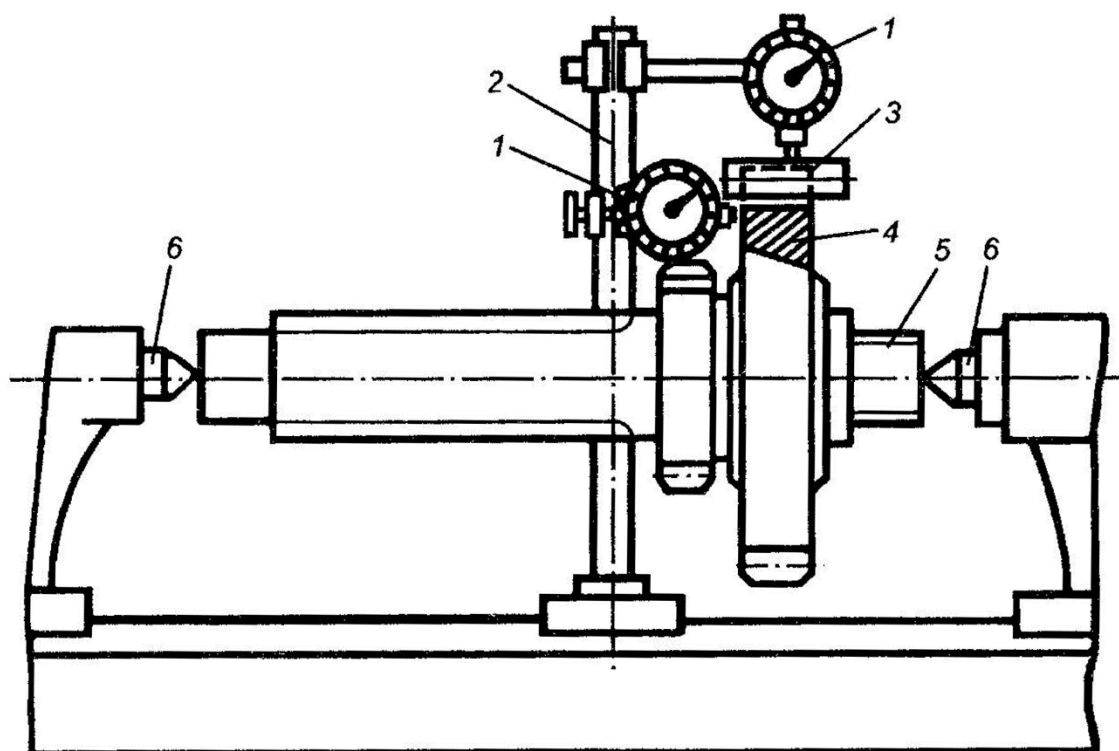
Схема пристосування для вимірювання радіального і осьового биття зубчастого колеса: 1 - індикатор; 2 - індикаторна стійка; 3 - валик контрольний; 4 - контрольоване зубчасте колесо; 5 - вал; 6 – центр
